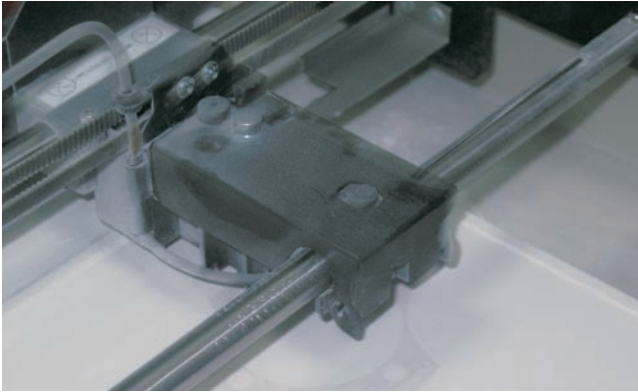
Stanowisko do wykonywania prototypów techniką 3DPrinting
